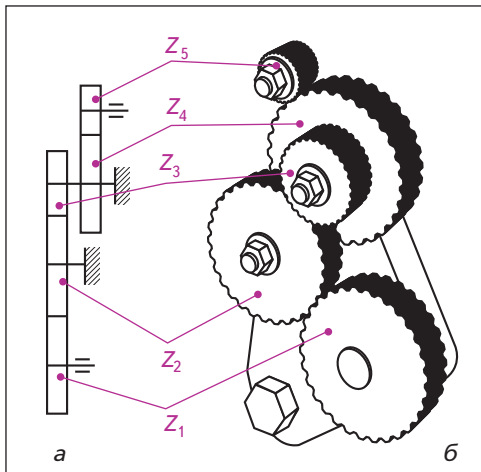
Кинематическая схема гитарного механизма токарно-винторезного станка (а) и его наглядное изображение (б)
